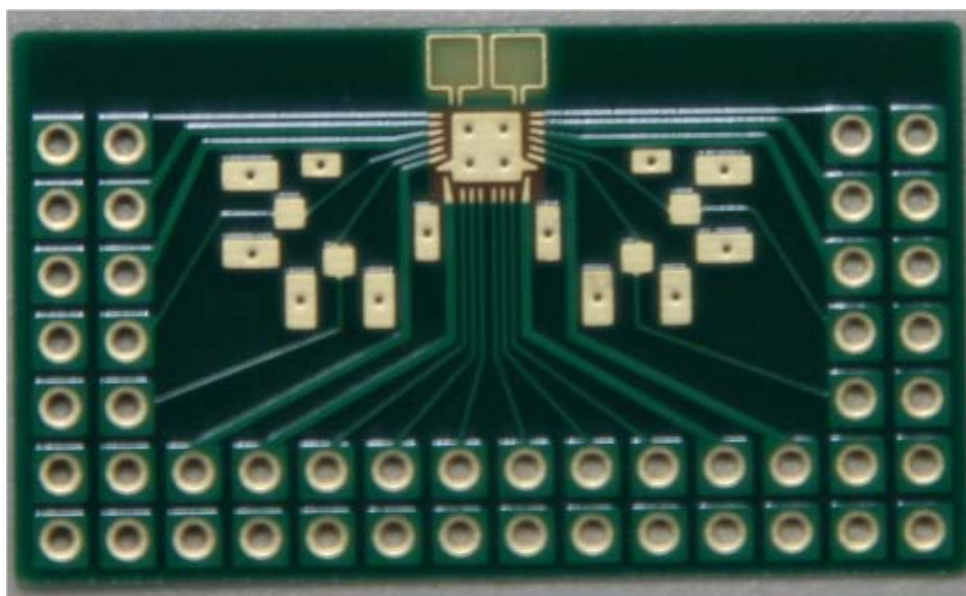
ディファレンシャルインダクティブカップリングのための PCB 写真
